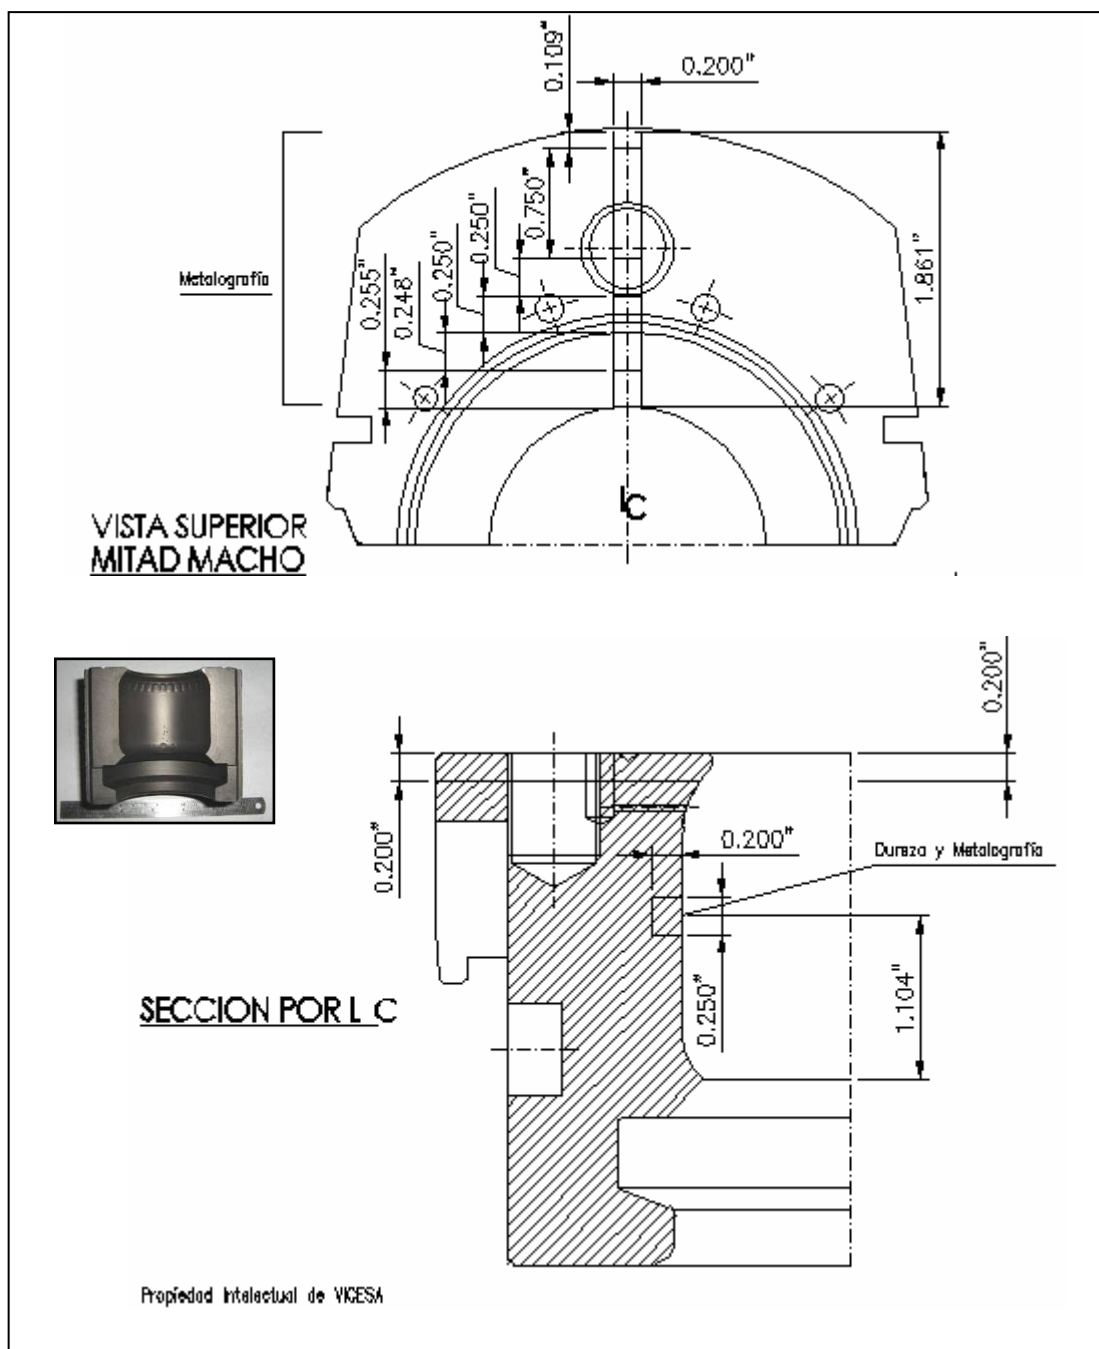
Dibujo del molde de la Moldura C-1615, y en el recuadro la fotografía de este.
